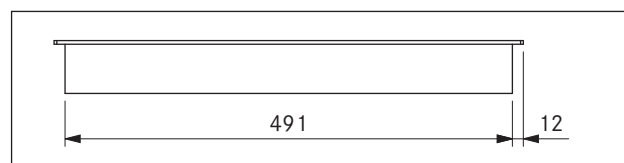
Dimensões do aparelho CKI, vista lateral
